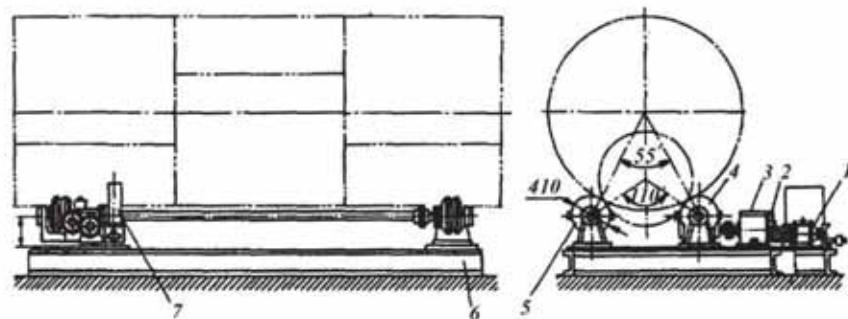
Роликовый сварочный стенд: 1 – электродвигатель; 2 – сменные зубчатые колеса; 3 – редуктор; 4,5 – приводная и холостая роликоопора; 6 – рама; 7 – электромагнит
